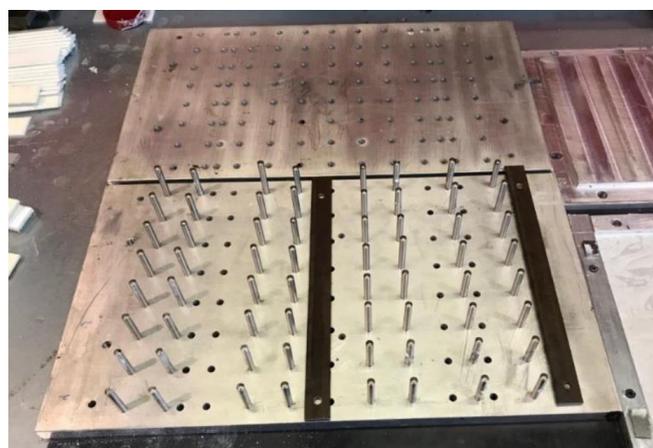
Dos partes del molde para la fabricación de las uniones SLJ
